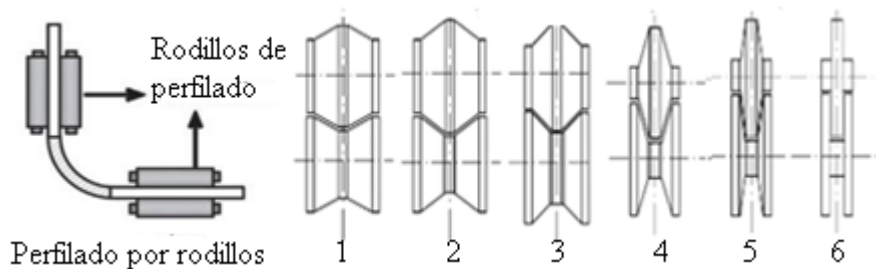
Formas de rodillos para cada etapa [8], [22].
